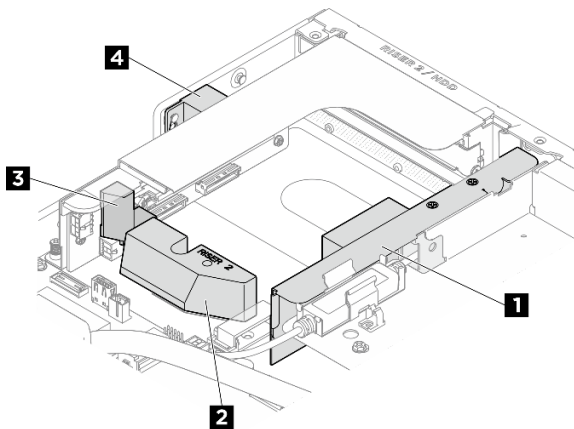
Position der DPU-Luftführung im Steckplatz für Adapterkarte 2
